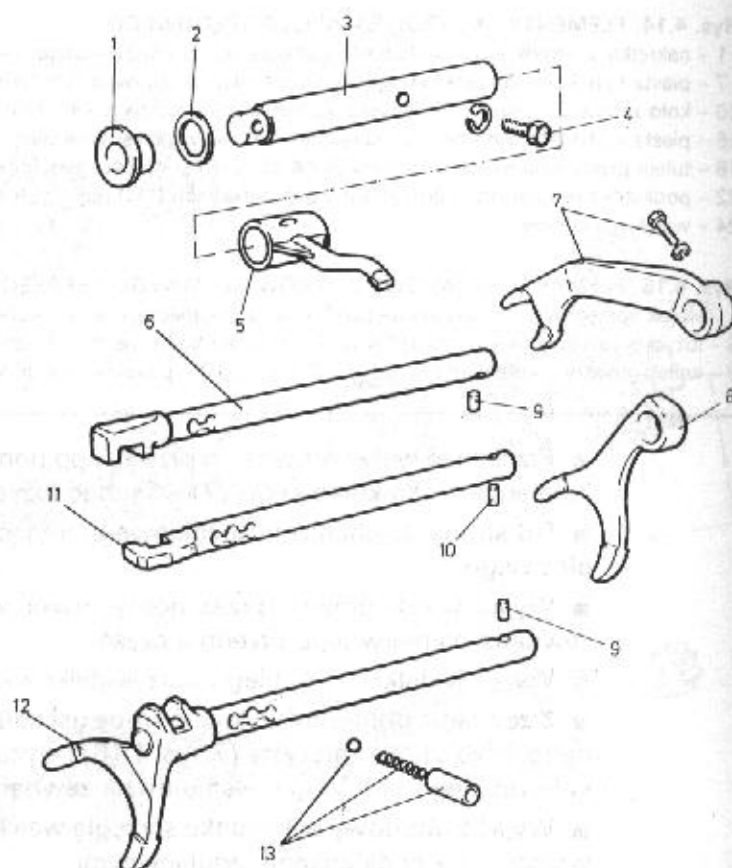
ELEMENTY SKŁADOWE WAŁKA BIEGU WSTECZNEGO
